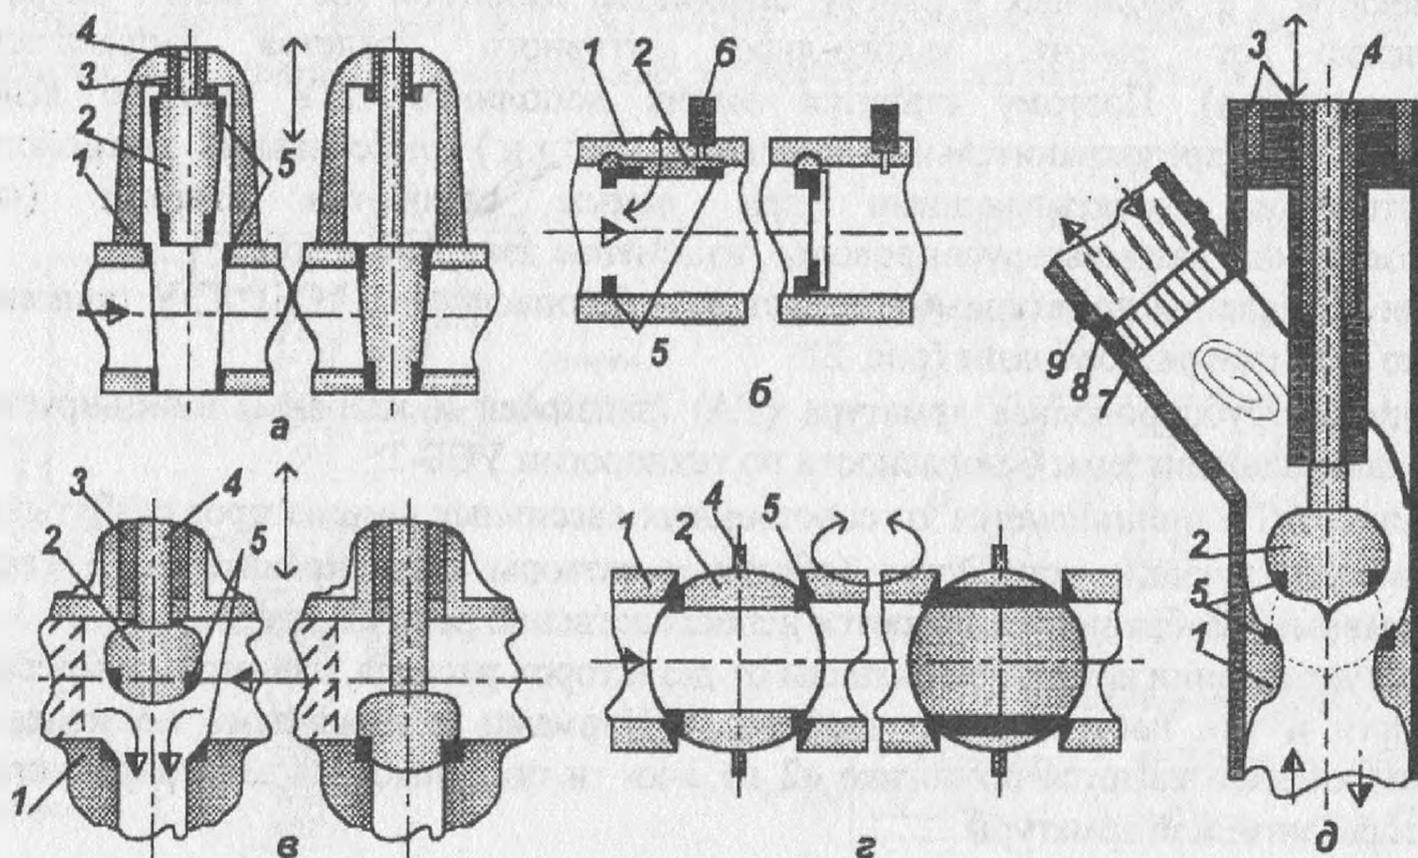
Проточная часть: а – задвижка; б – затвор обратный проходной (с указателем положения); в – клапан угловой (пунктир) или двухстороннего подвода (запорно-дрессельный, предохранительный); г – кран; д – клапан (отсекатель) с наклонным патрубком и вихревыпрямителем; 1 – корпус; 2 – затвор; 3 – уплотнение сальниковое; 4 – шток; 5 – уплотнение седла; 6 – указатель положения; 7 – вихревыпрямитель; 8 – сварной шов; 9 – фиксатор.
